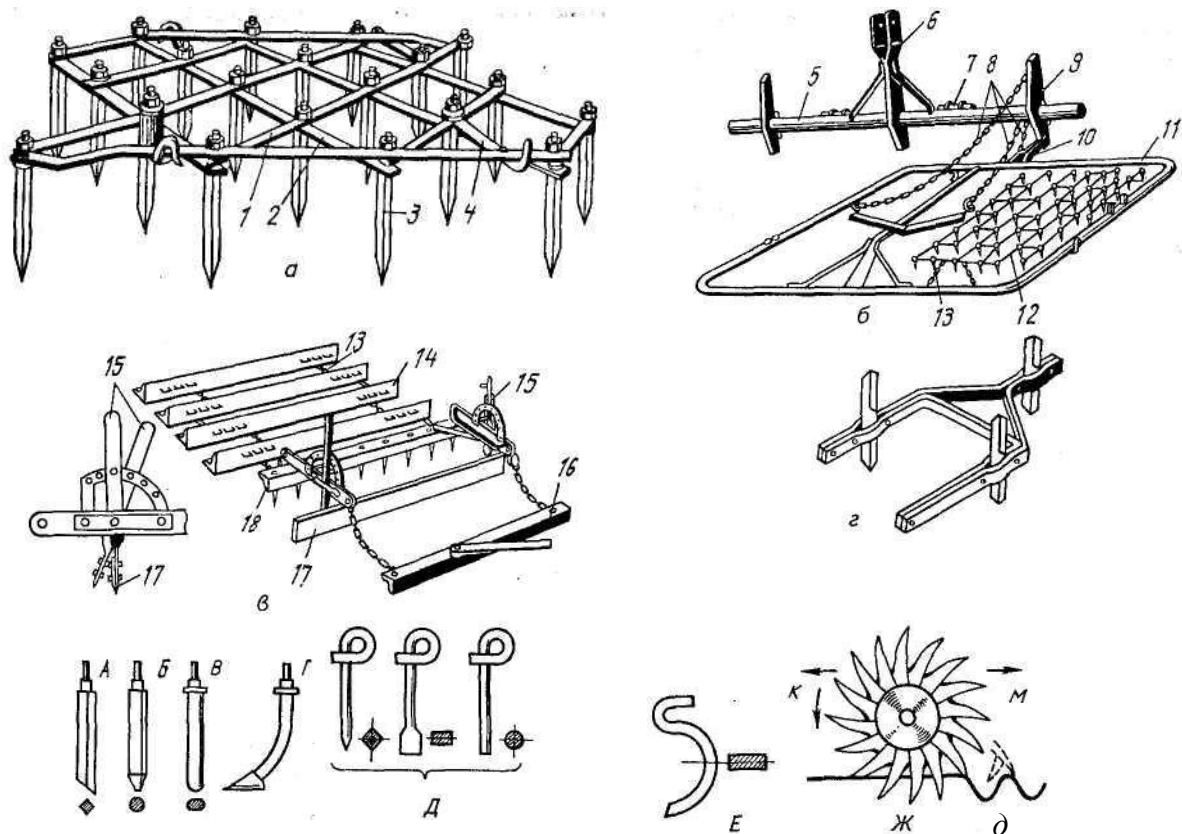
Бороны и их рабочие органы: а — зубовая БЗТС-1; б — сетчатая БСО-4; в — шлейф-бороны ШБ-2,5; г — звено луговой бороны с ножевидными зубьями; А — зуб квадратного сечения; Б — зуб круглого сечения; В — зуб овального сечения; Г — лапчатый зуб; Д — зубья сетчатой бороны; Е — зуб пружинной бороны; Ж — игольчатый диск мотыги; 1, 2, — планки рамы; 3 — зуб; 4 — прицепное устройство; 5 — брус навески; 6 — стойка; 7 — палец; 8, 13 — цепи; 9 — кронштейн; 10 — тяга; 11 — рамка; 12 — сетчатое полотно; 14 — шлейф; 15 — рычаг; 16 — вага; 17 — нож; 18 — грабли
